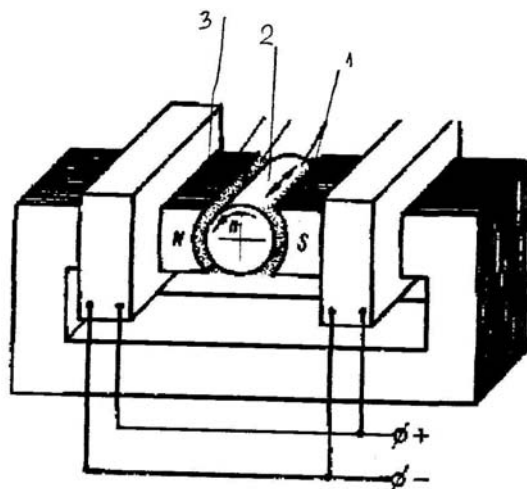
Схема магнитно-абразивной обработки наружных поверхностей вращения:
